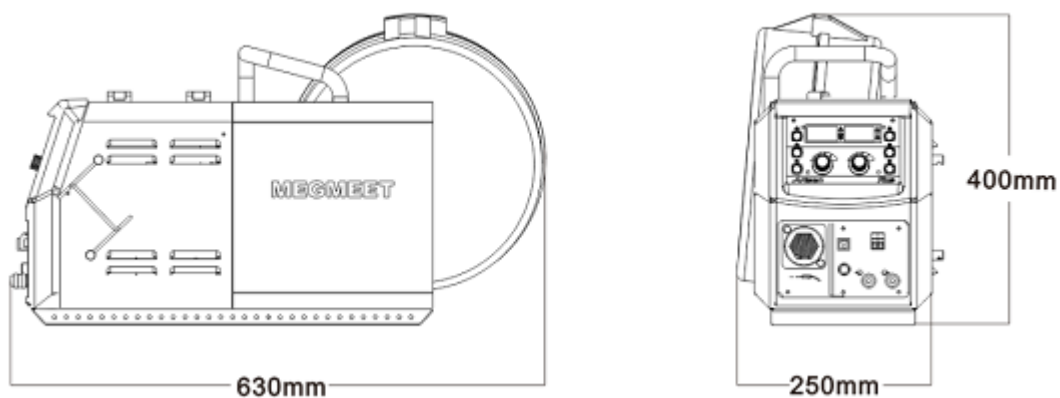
Габаритные размеры стандартного блока подачи проволоки.
